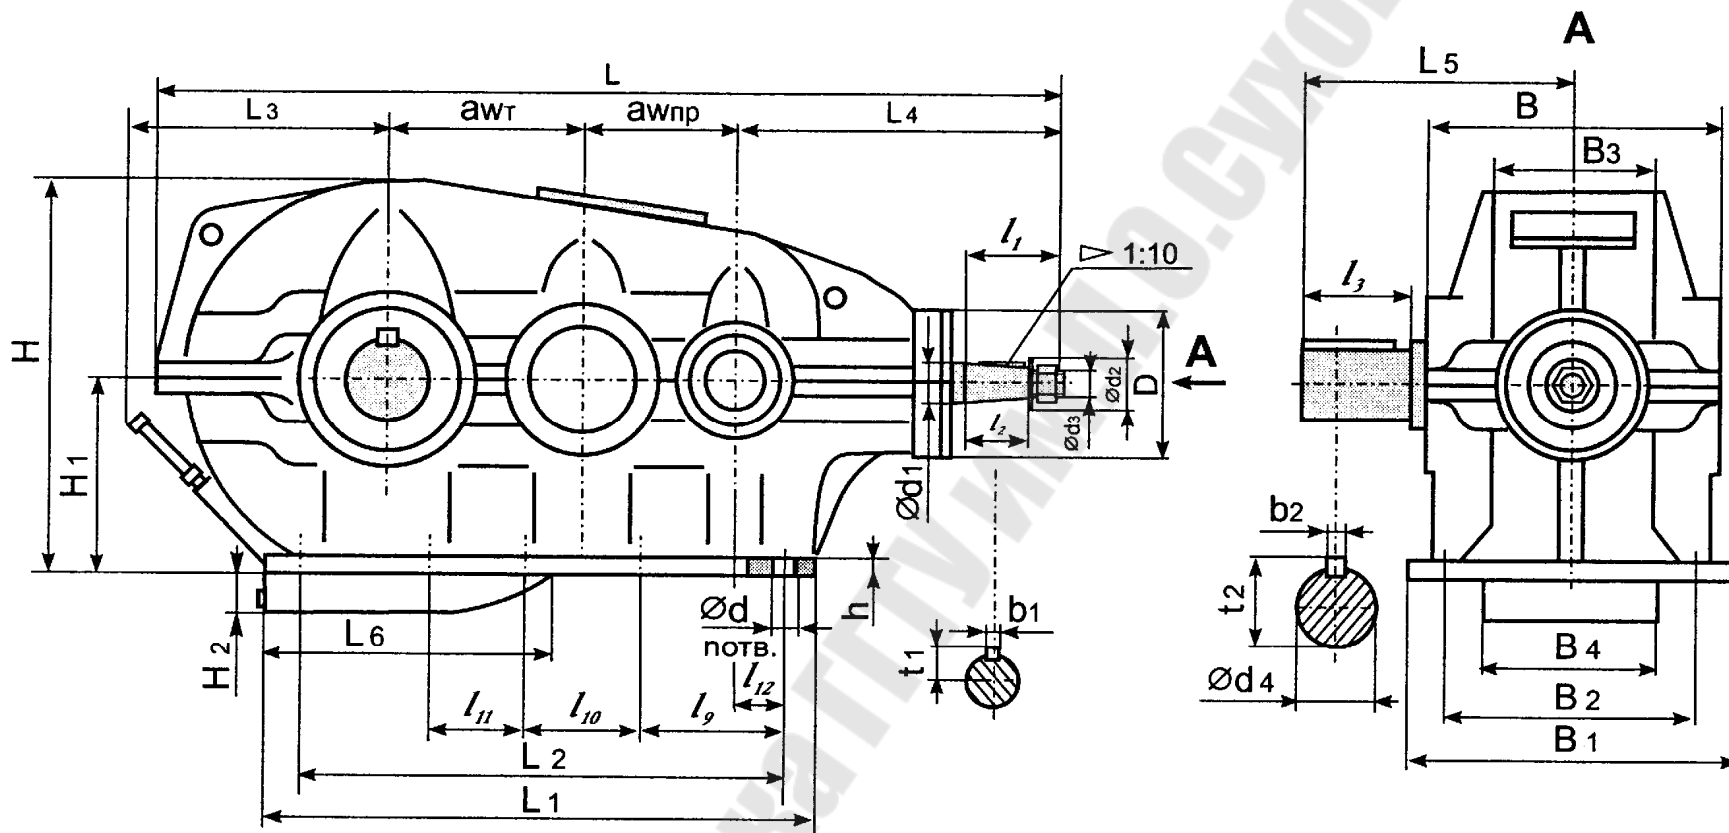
Редуктор коническо – цилиндрический трехступенчатый
